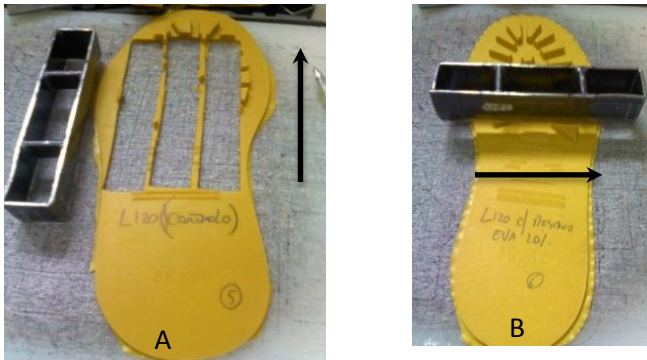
A: Corte das solas longitudinais; B: Corte das solas transversais.
